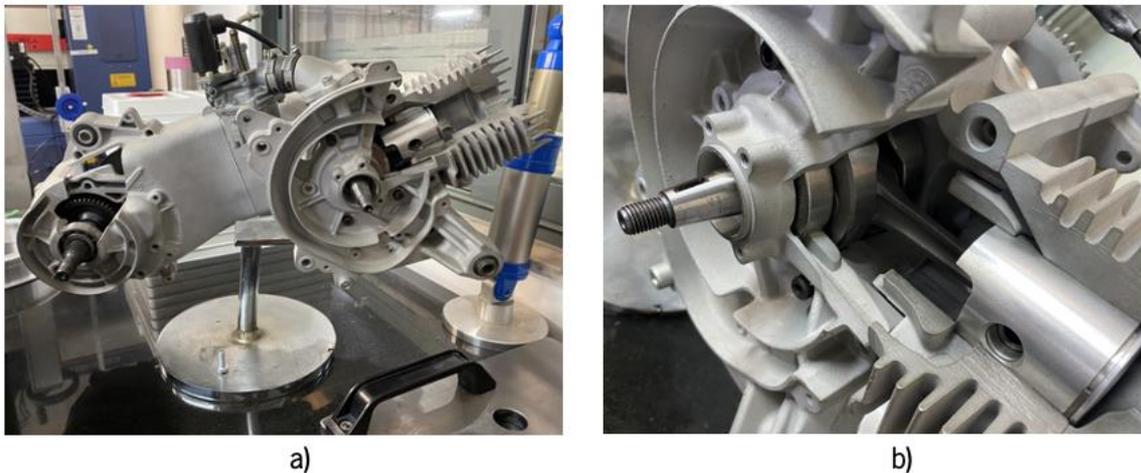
Motor de uma scooter (a) e Cambota inserida no motor (b)
